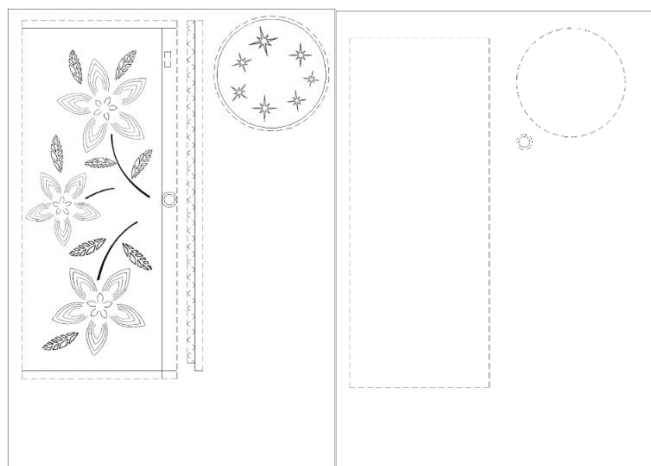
Шаблони кожуха для виготовлення корпусу.
